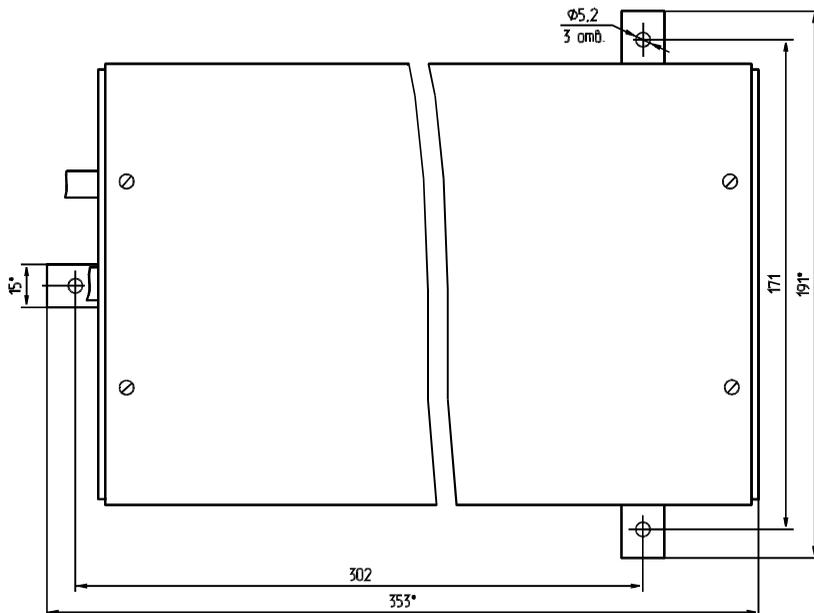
Габаритные и присоединительные размеры БПВРа
